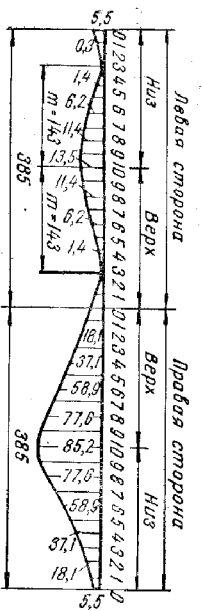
Развертка конуса отростка сварного тройника.
